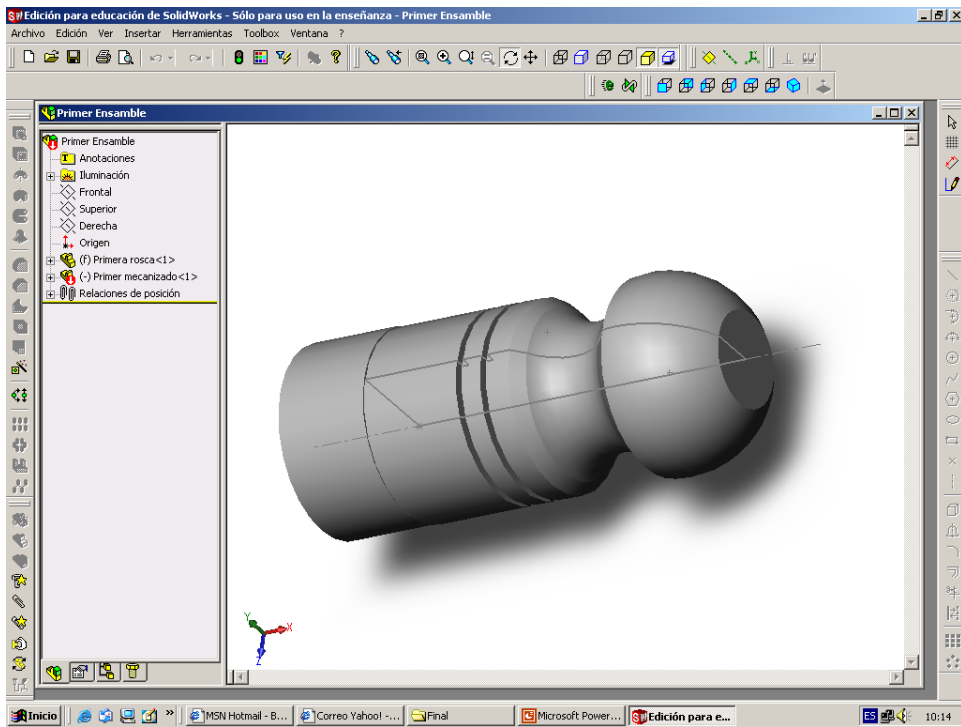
Perfil revolucionado – sujetador para puertas de baños
